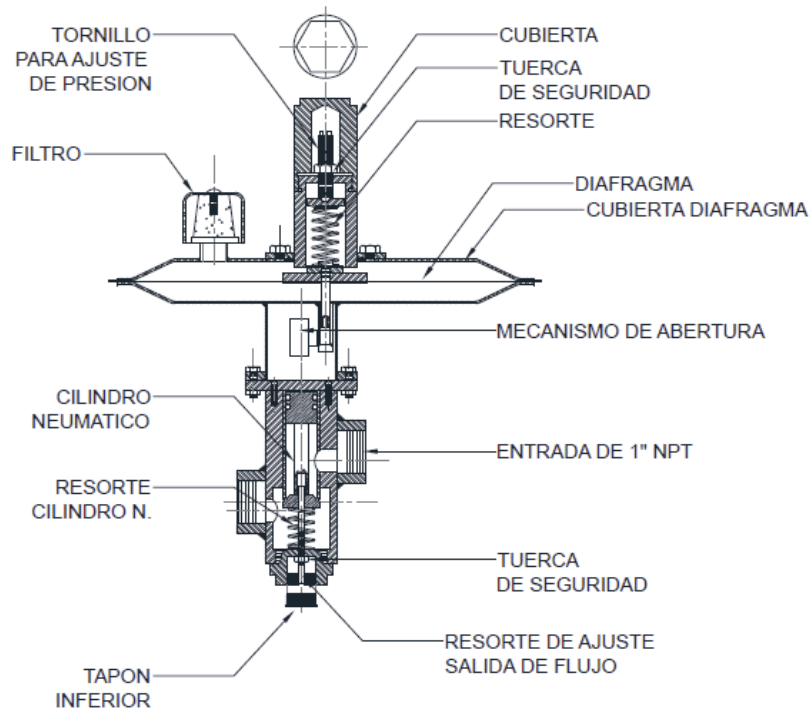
Partes de Válvula de Alivio Tank Blanketing Serie 1080⁽²⁴⁾.
